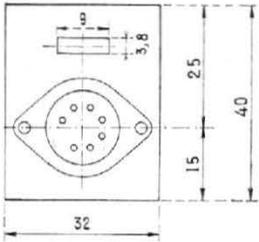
Le châssis élémentaire E de la figure d'ensemble. Il porte le transistor AF115 et le support pour le mandrin à sept broches
